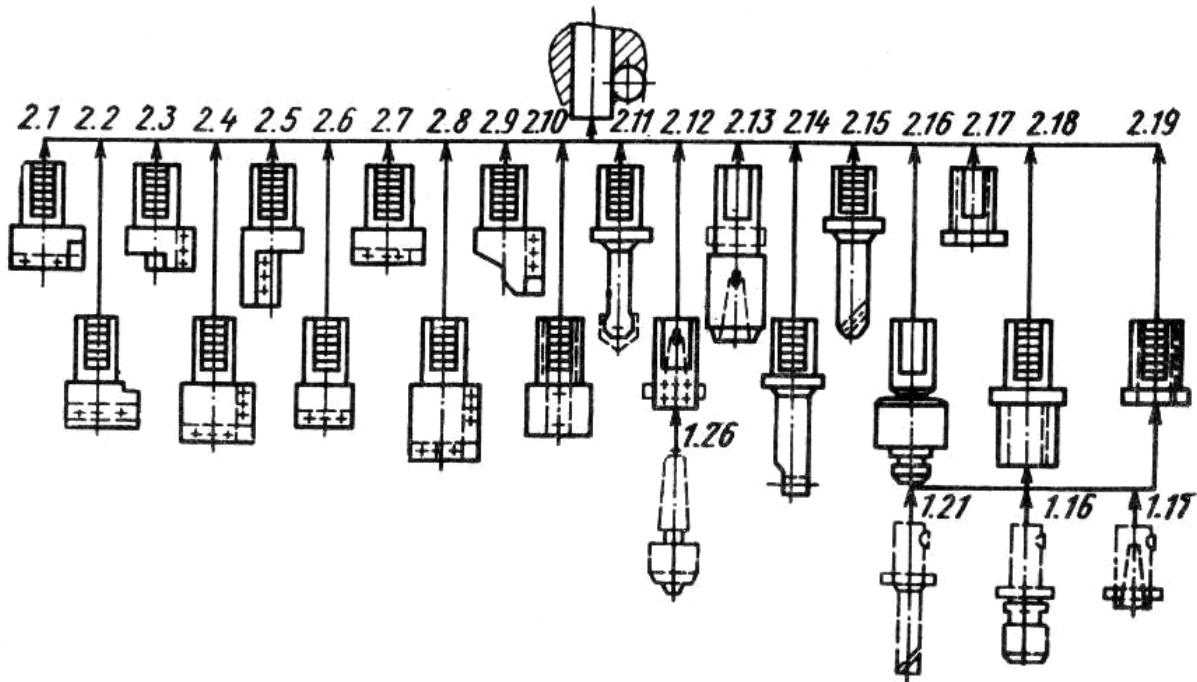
Схема соединения резцедержателя с цилиндрическим хвостовиком с револьверной головкой
